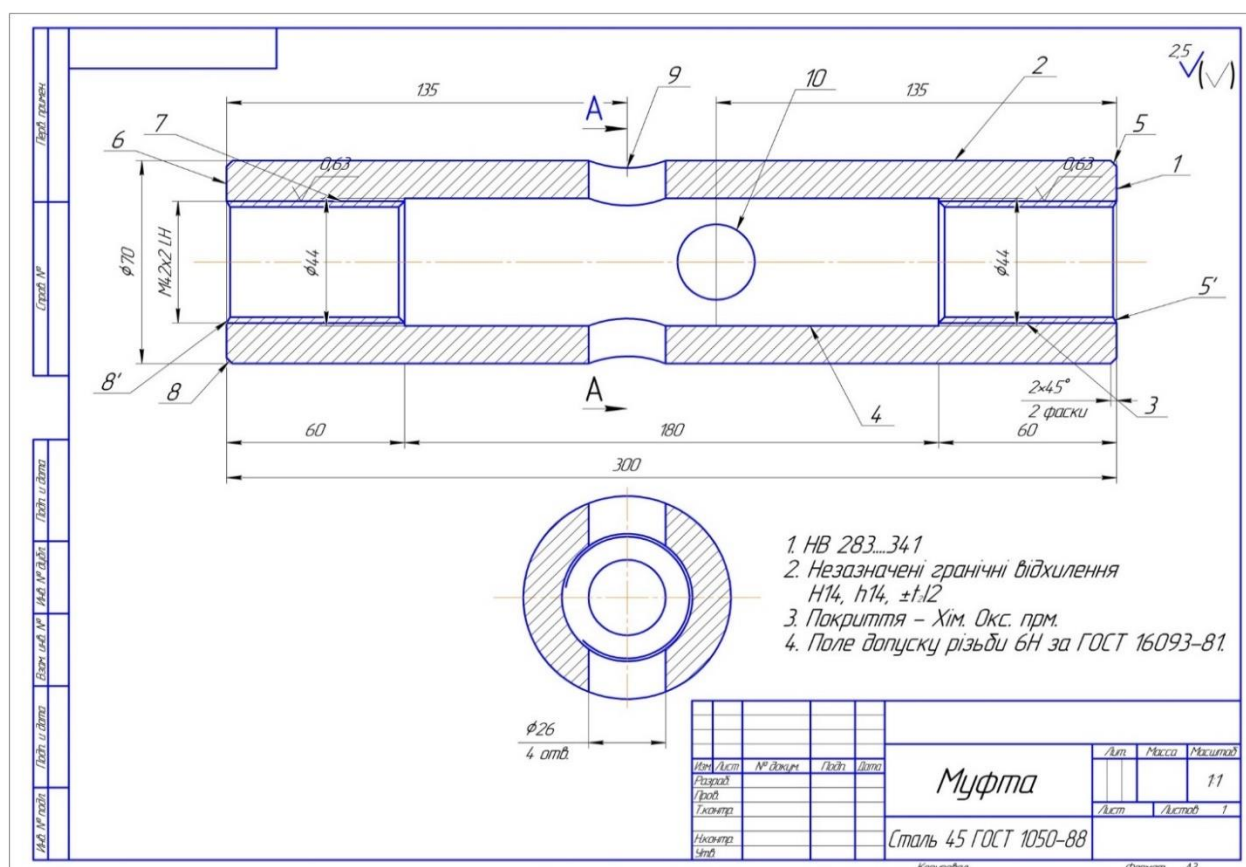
Креслення деталі-представника з нумерацією оброблюваних поверхонь
